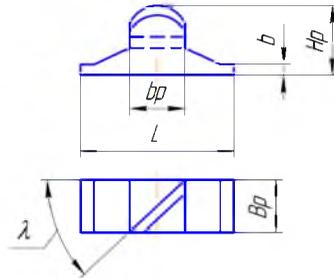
Конструкция вставного резца-зуба развёртки
